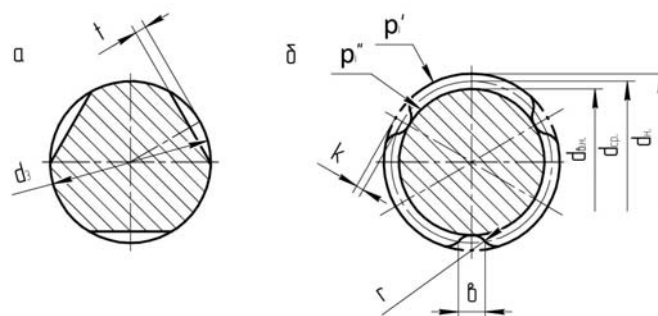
Поперечные сечения рабочей части трехгранных заготовок ПДМ: а – начальное, перед формированием резьбового профиля; б – после накатывания резьбового профиля на рабочей части
